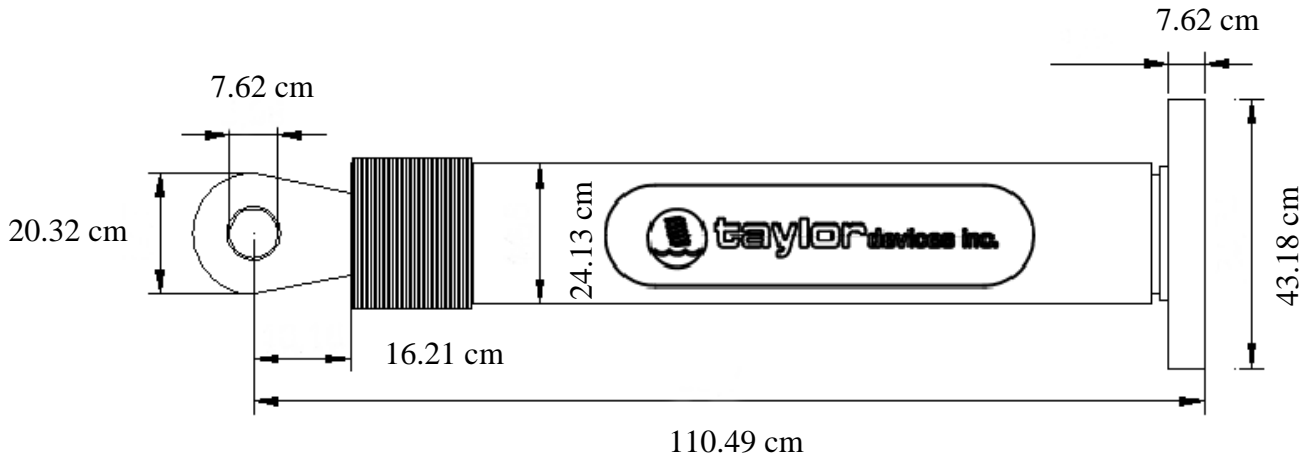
Dimensiones de la placa base del dissipador de 220 kip
